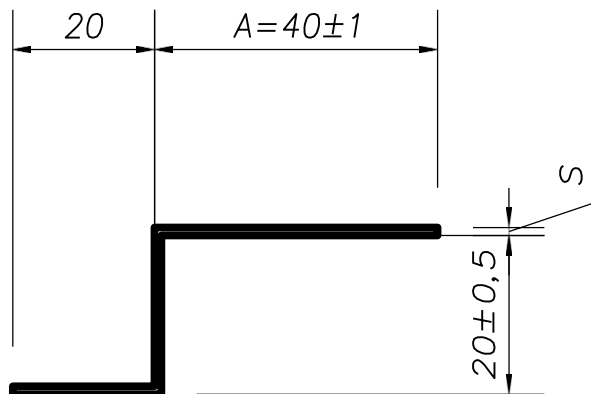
Профиль вертикальный Z-образный промежуточный (П ZВП)
